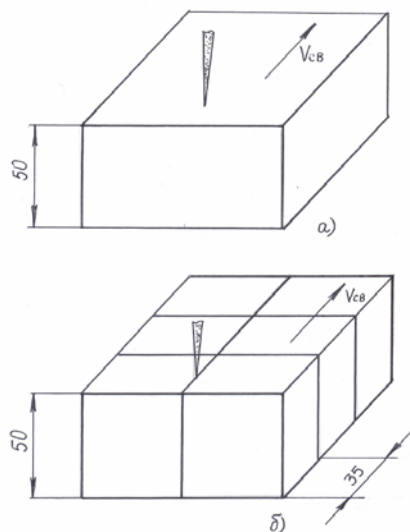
Схема сборки образцов под сварку: а – по целому материалу; б – по составному образцу
